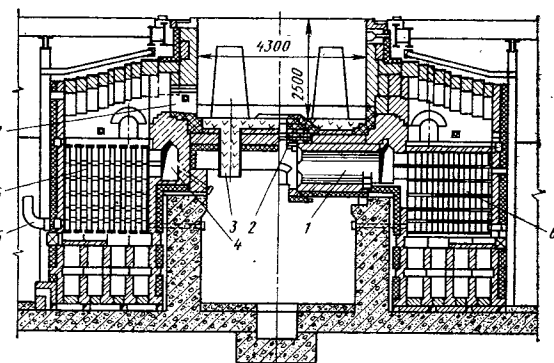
Рекуперативный нагревательный колодец с отоплением из центра подины (крышка снята);
